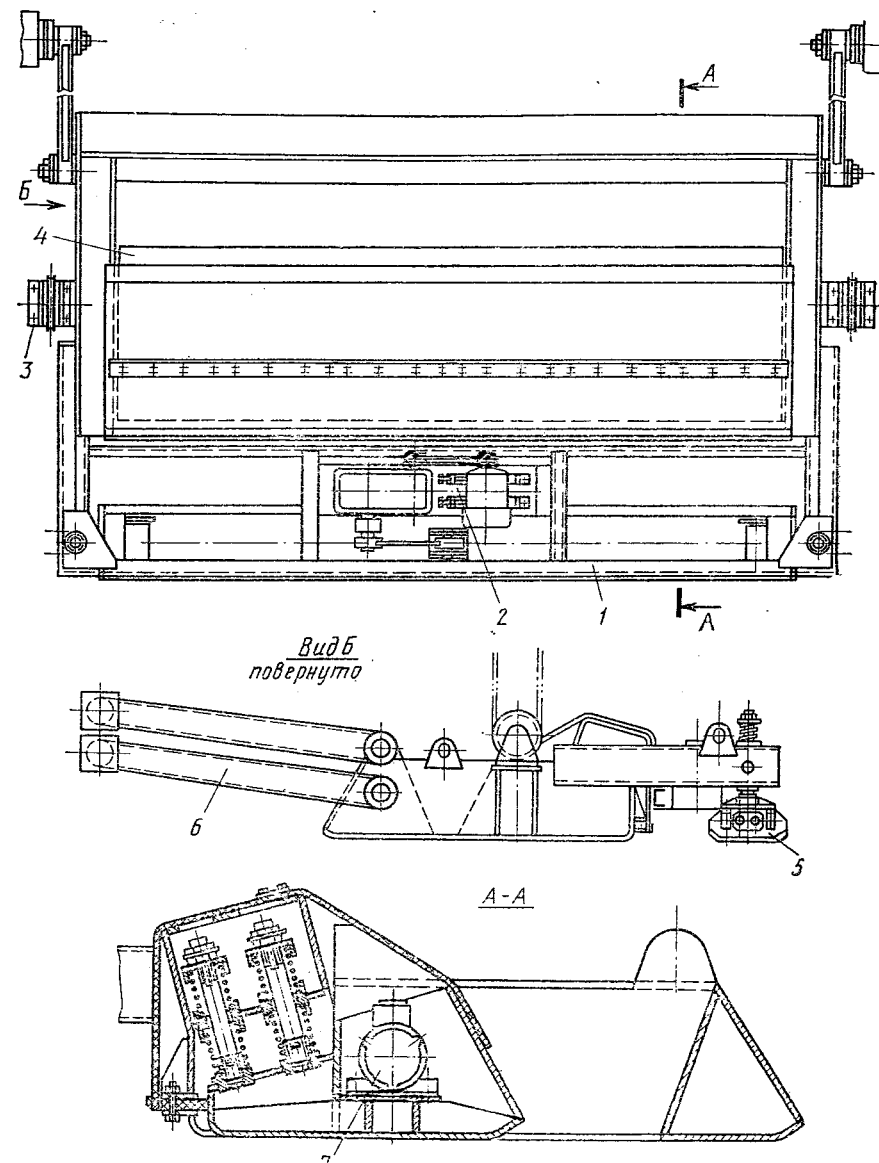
Вибронасадок бетоноукладчика СМЖ-162А:
